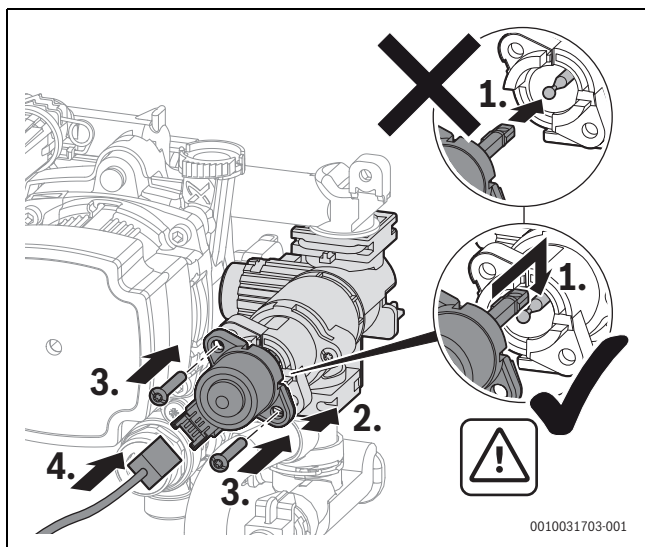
Montar el motor de la válvula de 3 vías (variante con tornillos)
